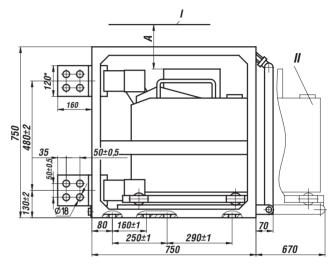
Габаритные и установочные размеры выключателей 306В в двух- и трехполюсном исполнении
